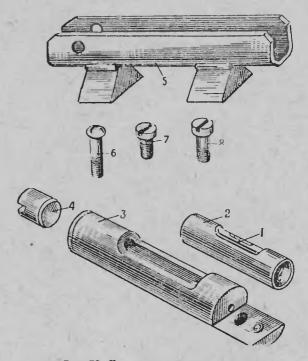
Детали контрольного уровия: 1 — ампула уровня АЦП 60" — 11×54; 2 — оправка ампулы; 3 — трубка; 4 — пробка; 5 — корпус уровня; 6 — винт; 7 — винт; 8 — винт
